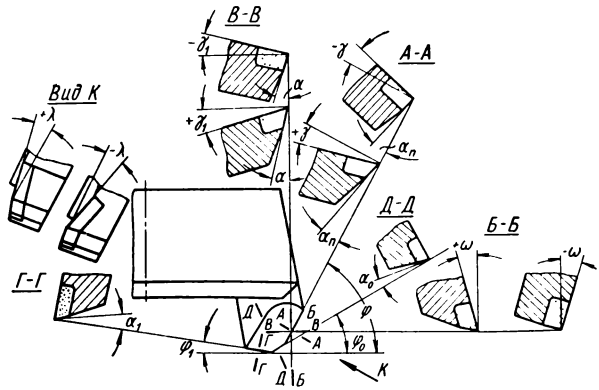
Геометрические параметры режущей части торцовой фрезы с пластинками из твердого сплава
